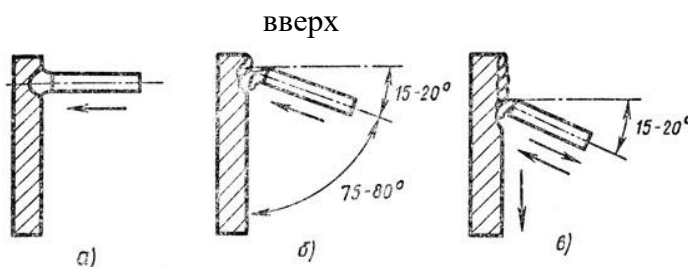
Схема техники сварки (наплавки) на спуск: а - зажигание дуги, б - образование сварочной ванны, в - движение электрода вниз
